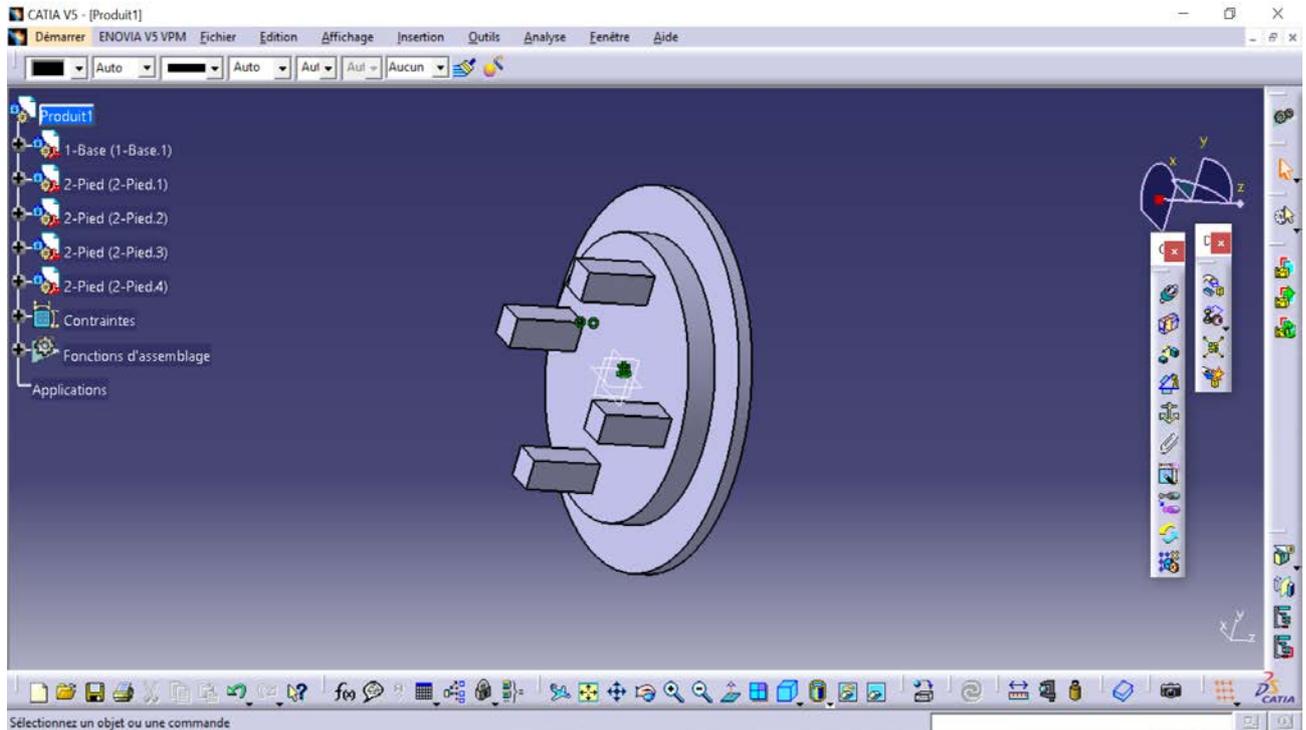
Assembly Design de l'ensemble Table Ronde [1], [2]
